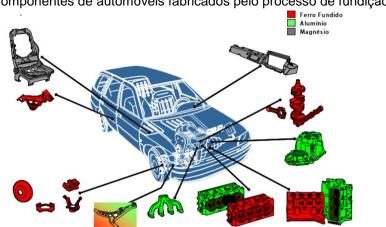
Componentes de automóveis fabricados pelo processo de fundição.
